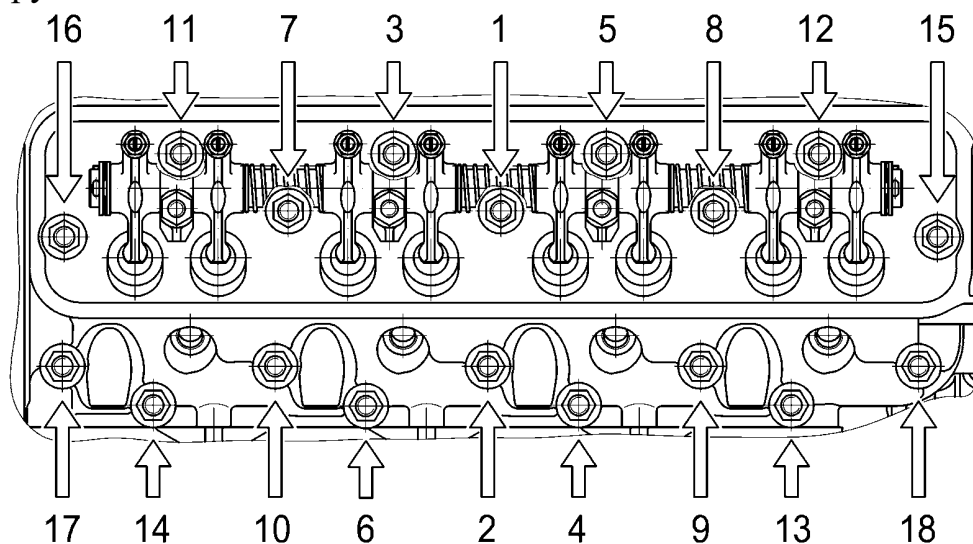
Порядок подтяжки гаек крепления головок цилиндров
